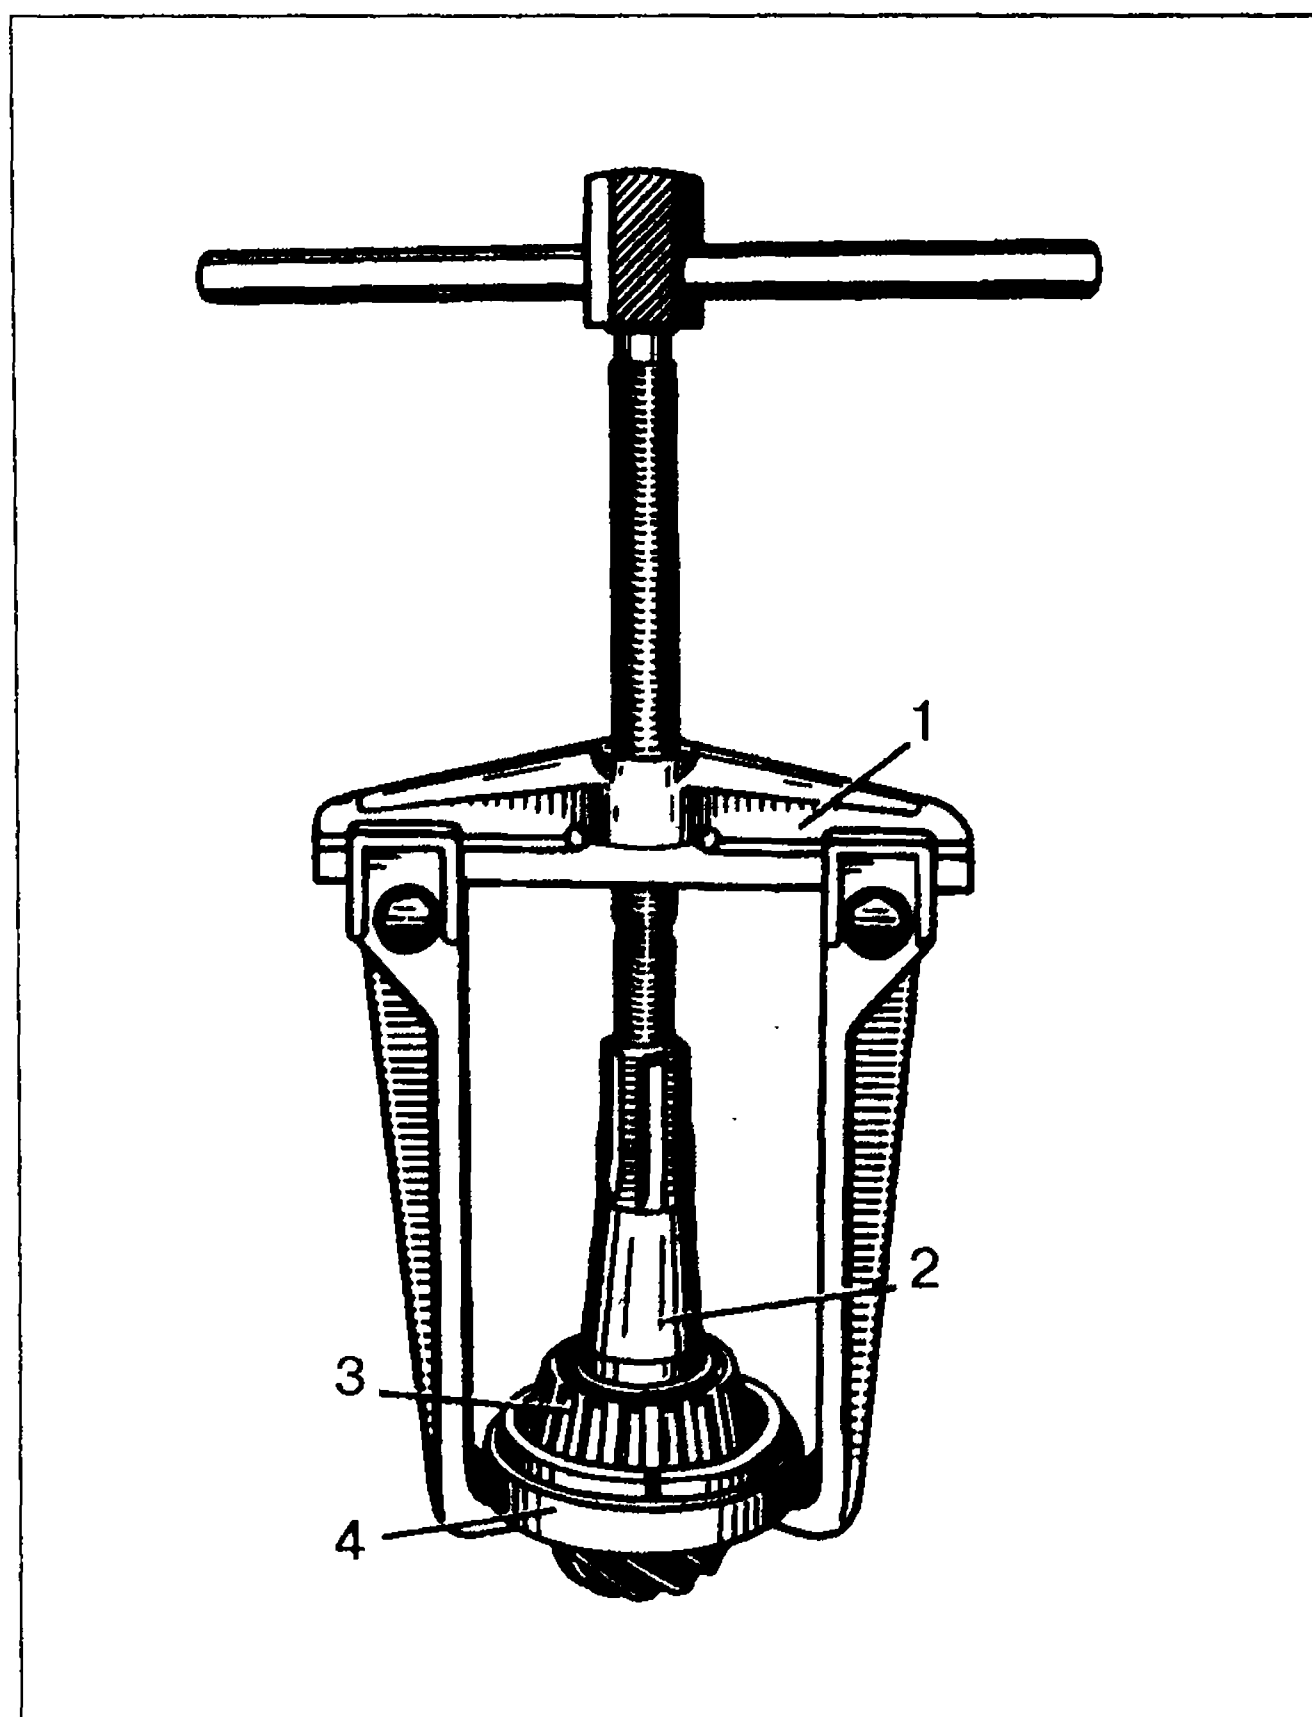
Снятие внутреннего кольца заднего подшипника ведущей шестерни универсальным съемником А.40005/1/7: 1-универсальный съемник А.40005/1/7; 2-ведущая шестерня; 3-внутреннее кольцо подшипника; 4-приспособление А.45008
